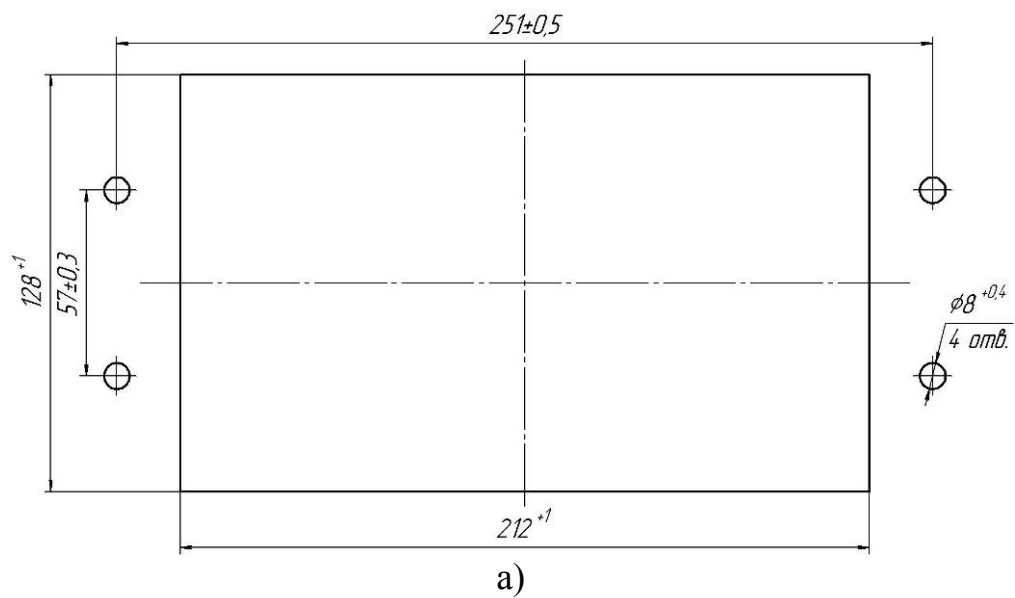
Установочные размеры для установки устройства изнутри шкафа:
